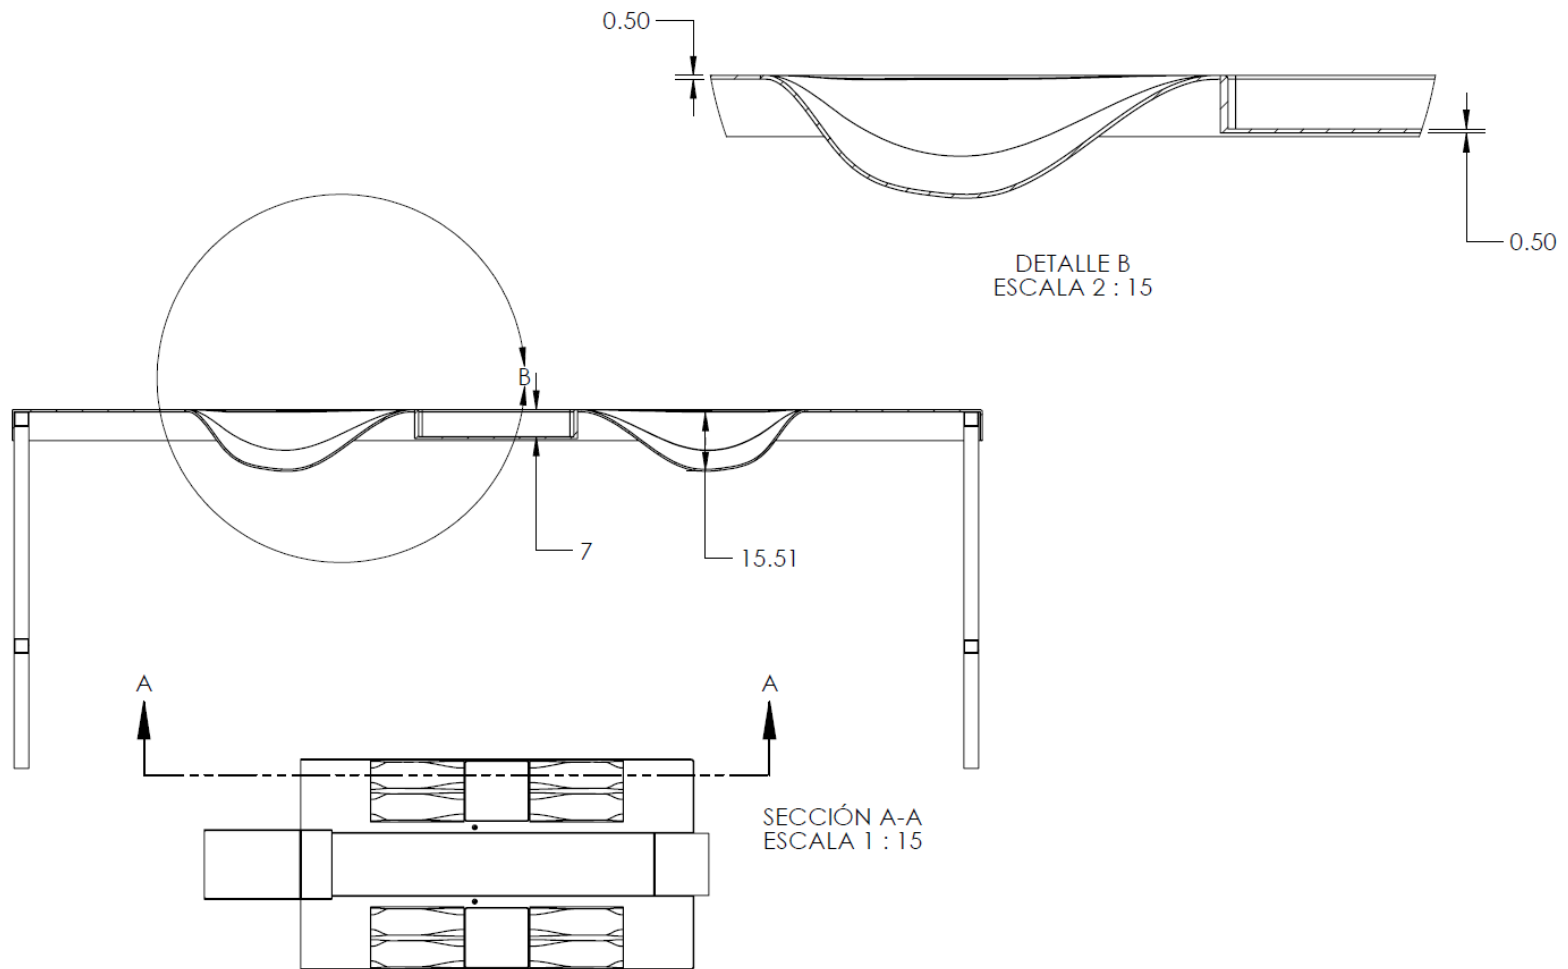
Detalle 2, Corte A - A, Tolva de sachets (Fuente propia)
